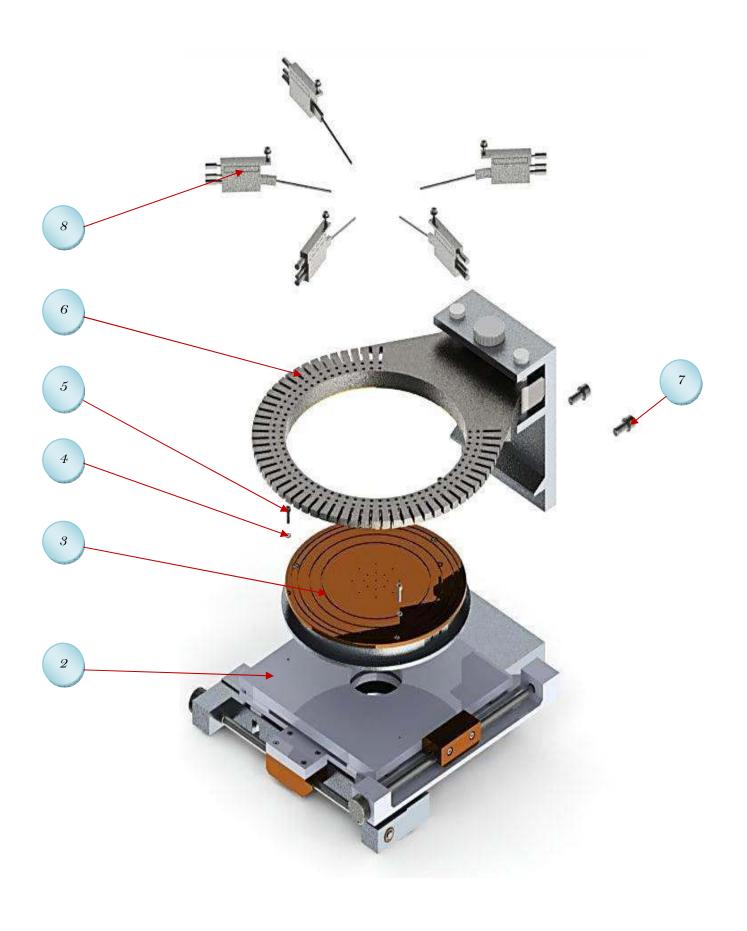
Vue éclatée de tester sous pointes, réalisé par solide Works
